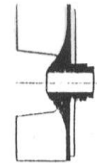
Offenes Zweikanalrad mit S-förmigen Schau-
